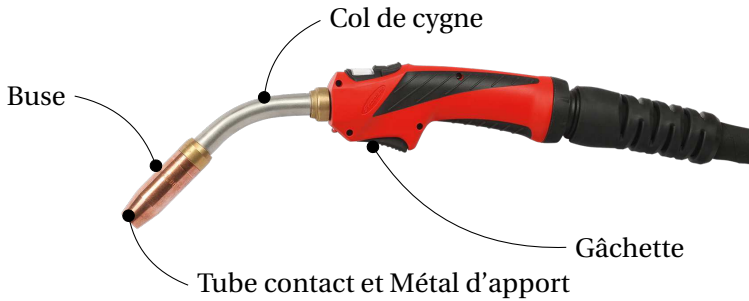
Torche de soudage MIG/MAG.
